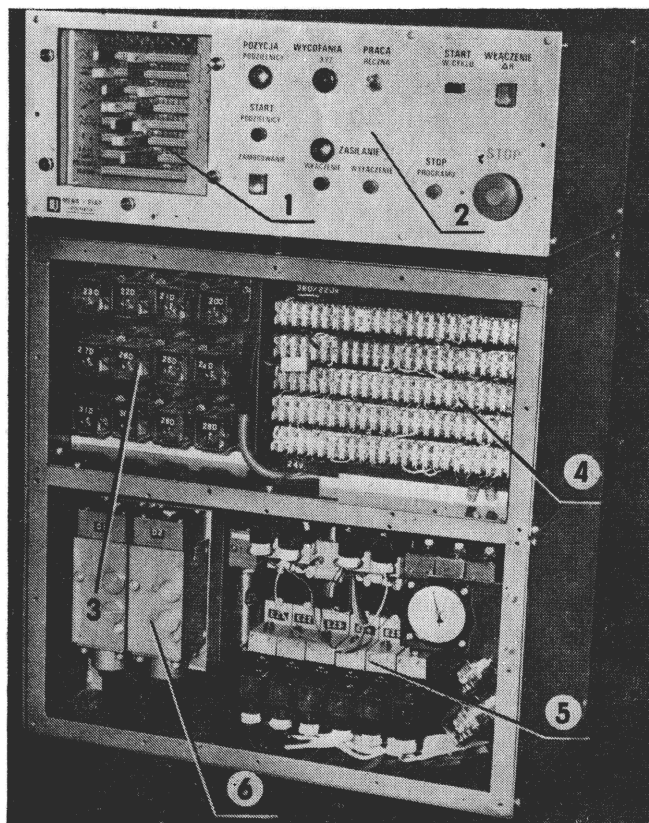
Innenraum des Schaltschranks mit Steuersystem
